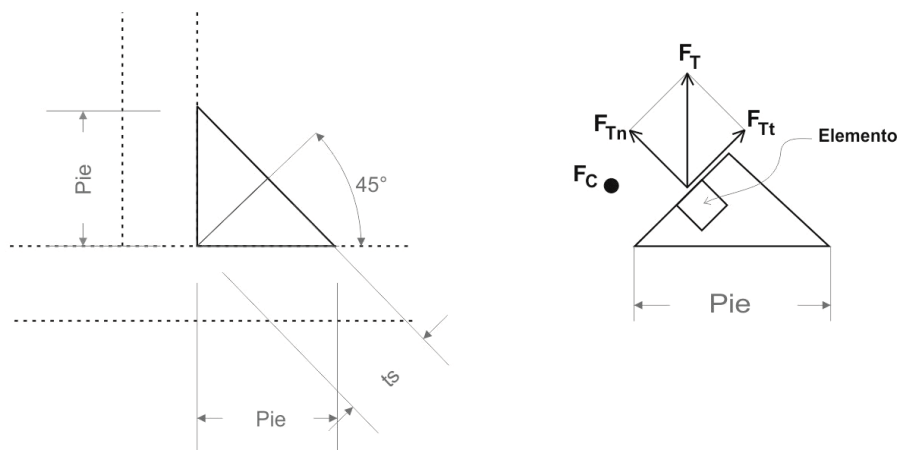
Detalle de la unión soldada tipo "tee-joint" y las fuerzas actuantes
